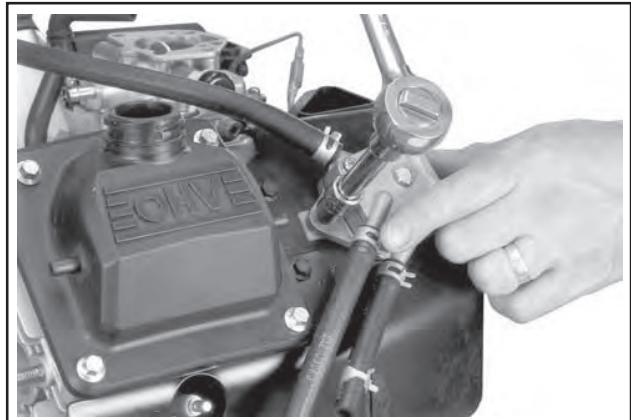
Die Befestigungsschrauben der Kraftstoffpumpe entfernen (Darstellung der Pumpe mit Metallgehäuse).
